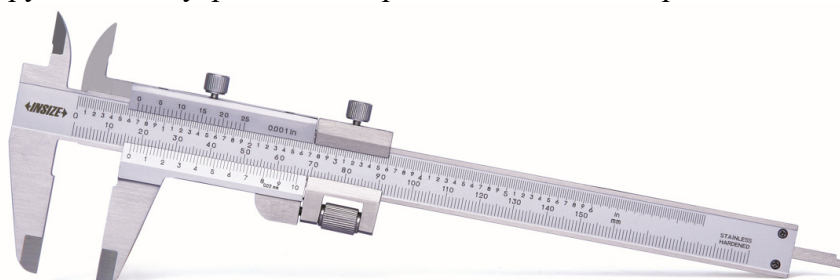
Общий вид штангенциркулей модификации 1233 исполнения 130, 180, 280
